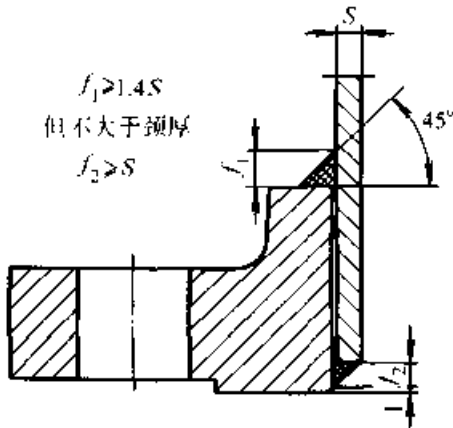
带颈平焊法兰与钢管连接的焊接接头
